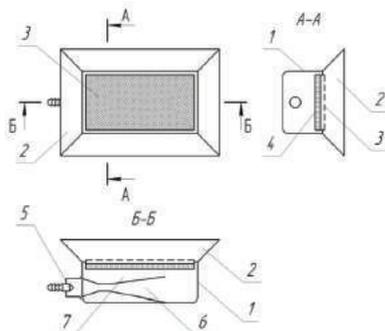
Схема устройства горелки инфракрасного излучения: 1 – корпус; 2 – рефлектор; 3 – сетка; 4 – керамический элемент (насадка); 5 – сопло; 6 – смеситель; 7 – распределительная камера.
